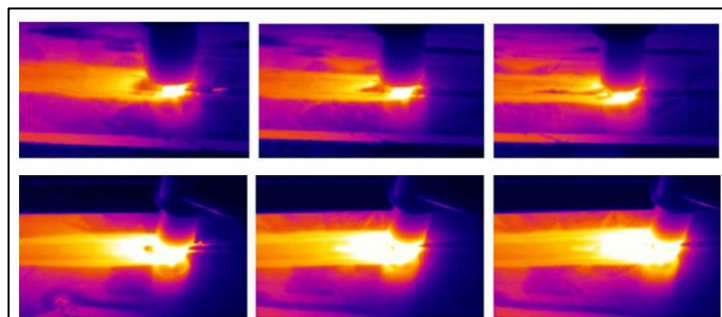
Aplicación de la termografía en el control de soldadura
